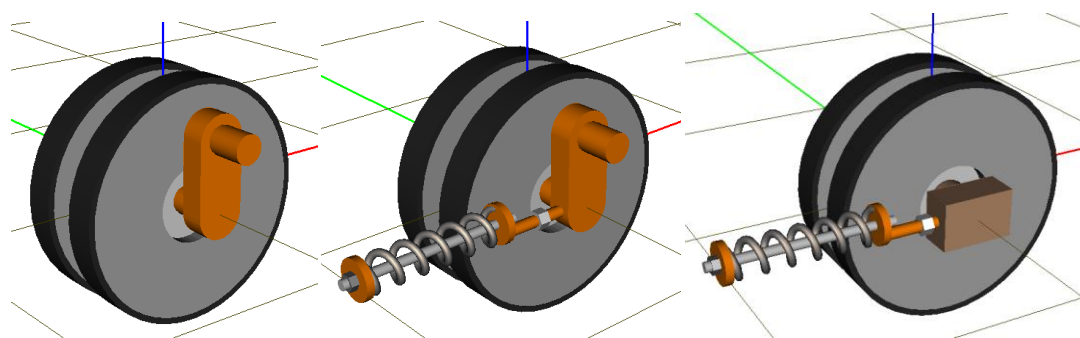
Стандартные модели направляющих колес с натяжным устройством
